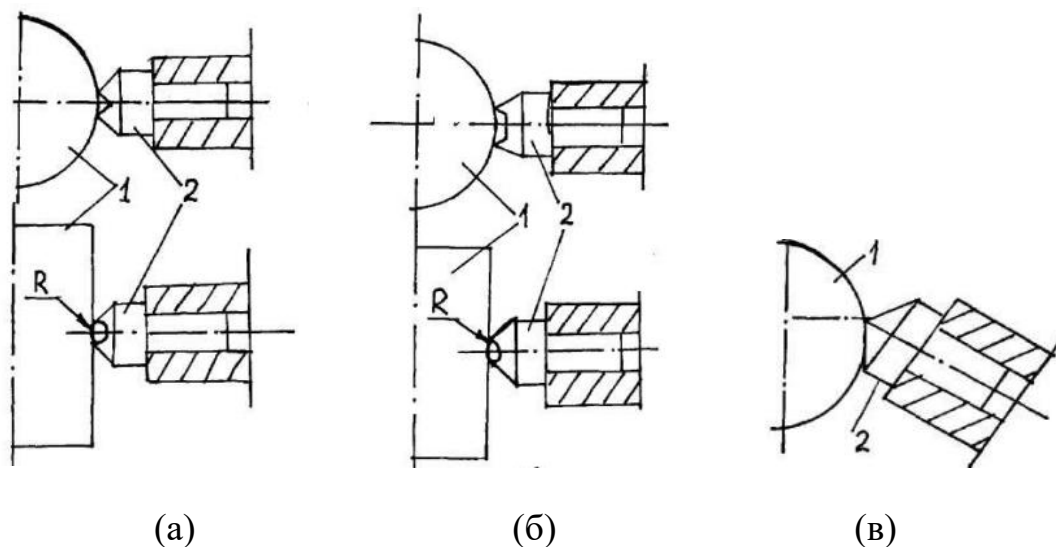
Схема установок выглаживателей при обработке цилиндрической поверхности: а – сферическая форма заточки, б – цилиндрическая, в – коническая; 1 –обрабатываемая поверхность, 2 – заточка.
